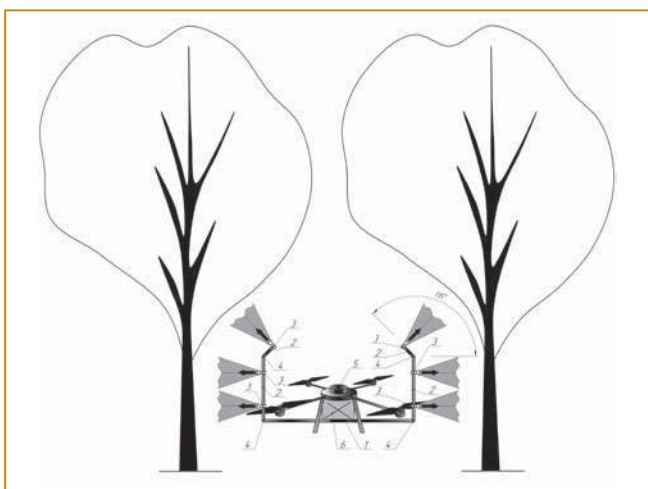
БПЛА вид спереди со штангой и рычагами, поднятым вверх и под углом
